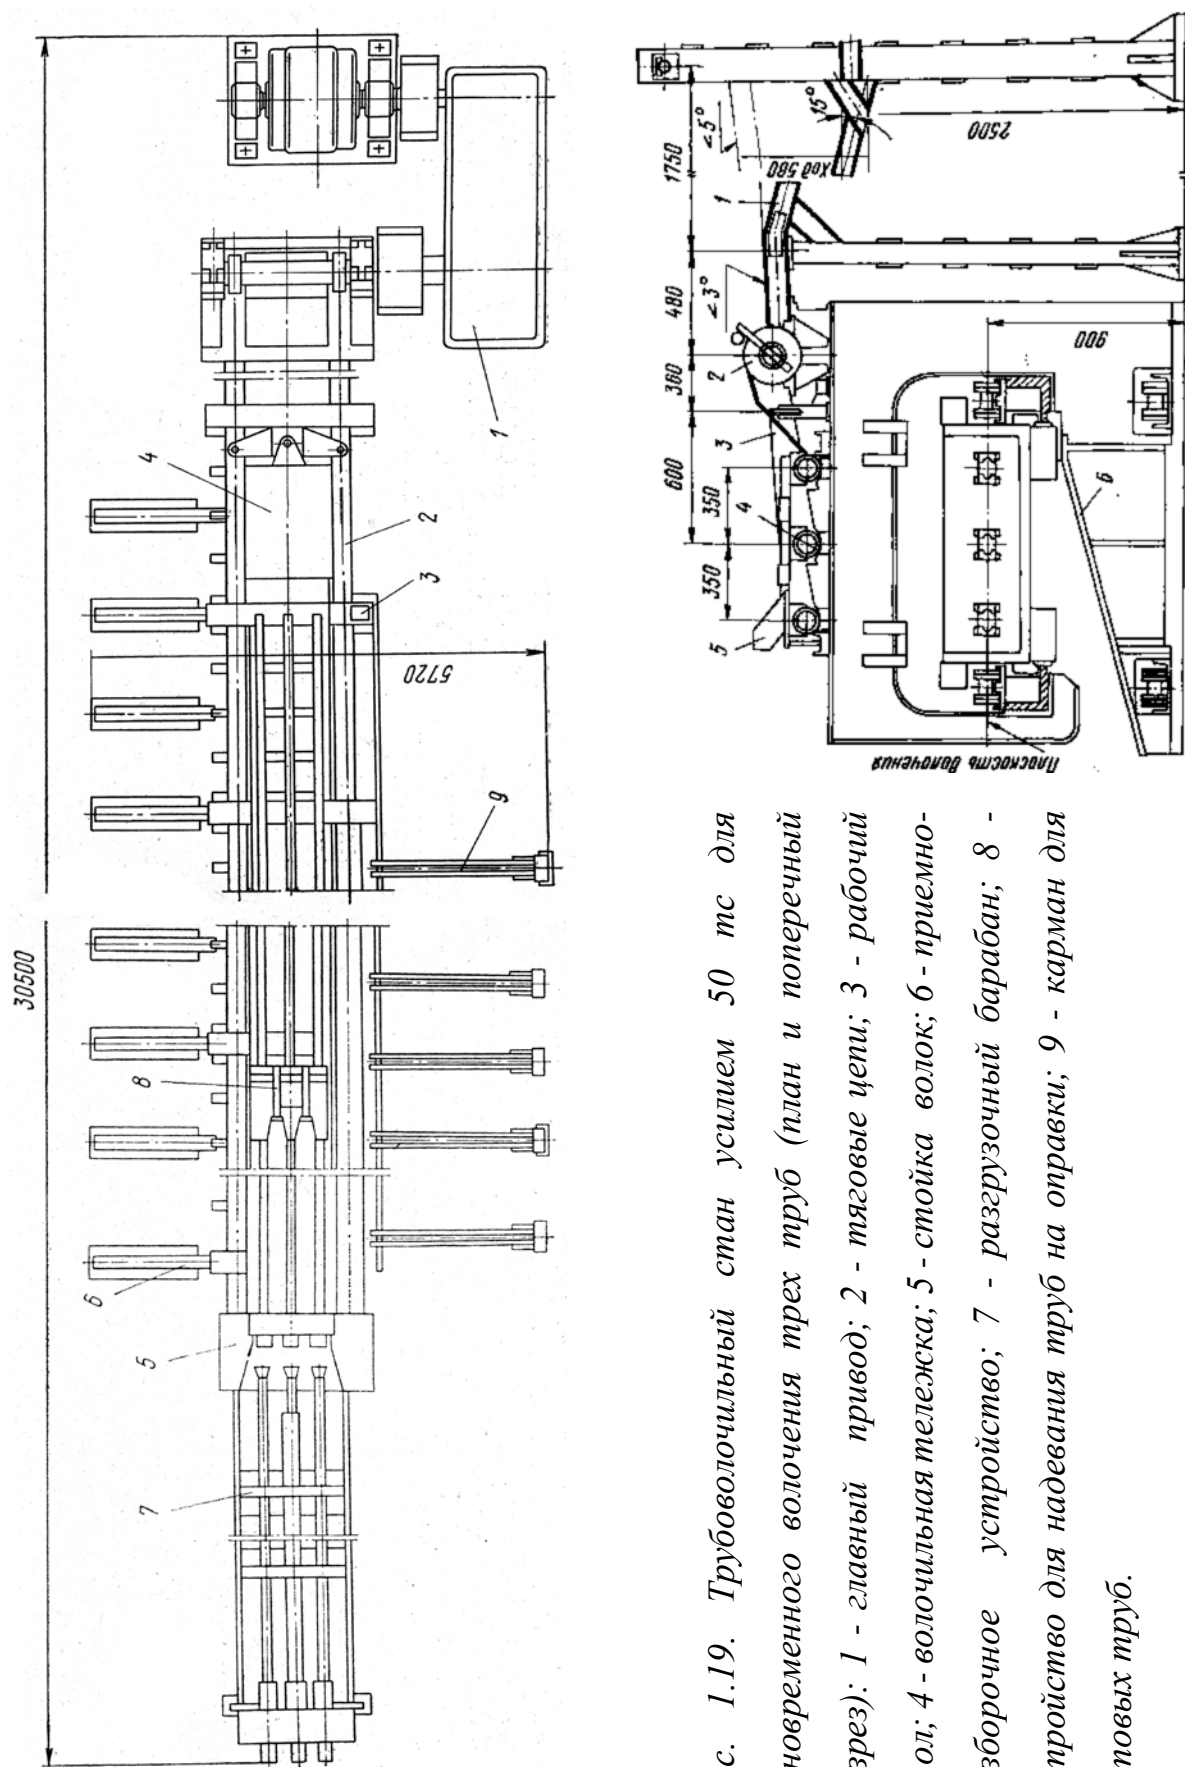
Трубоволоочильный стан усилием 50 тс для одновременного волочения трех труб (план и поперечный разрез): 1 - главный привод; 2 - тяговые цепи; 3 - рабочий стол; 4 - волоочильная тележка; 5 - стойка волок; 6 - приемно-разборочное устройство; 7 - разгрузочный барабан; 8 - устройство для надевания труб на оправки; 9 - карман для готовых труб.
